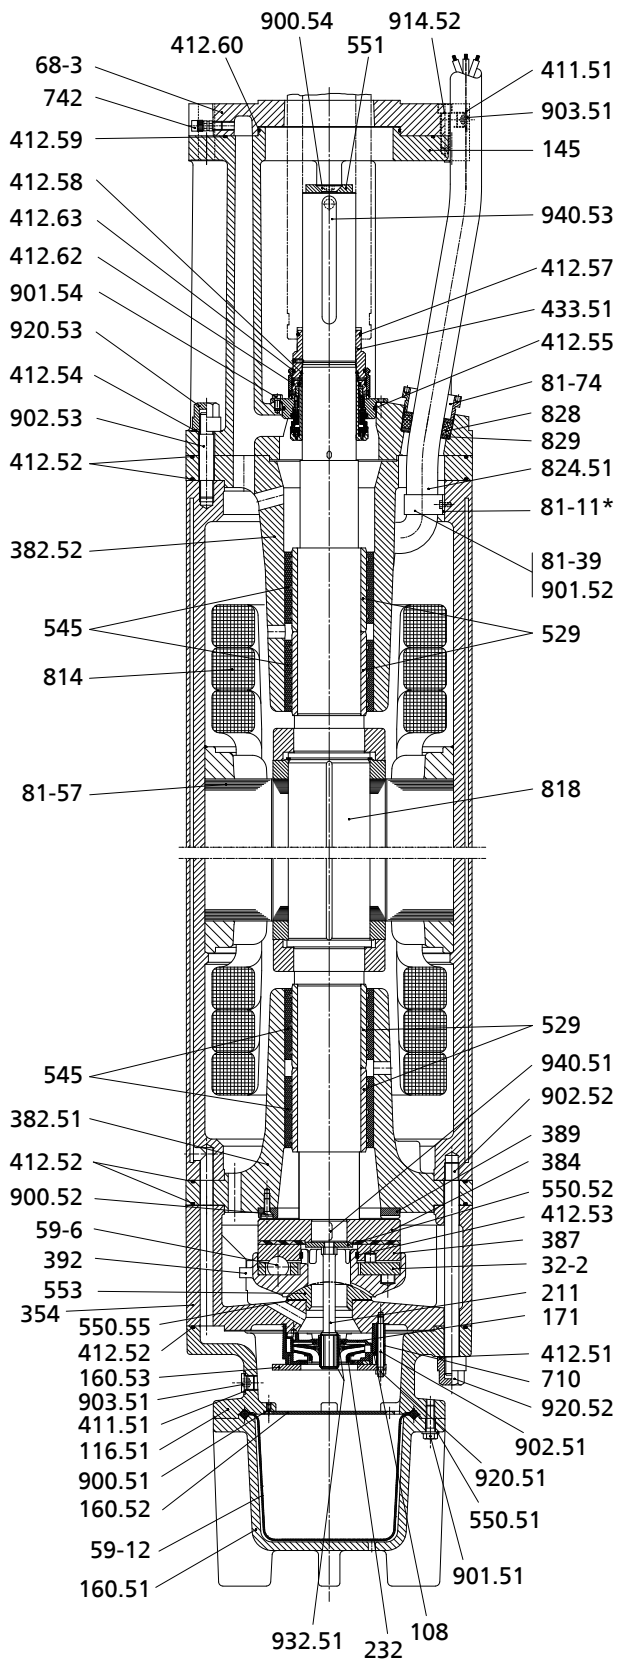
Компоновочный чертеж погружного двигателя V, X
